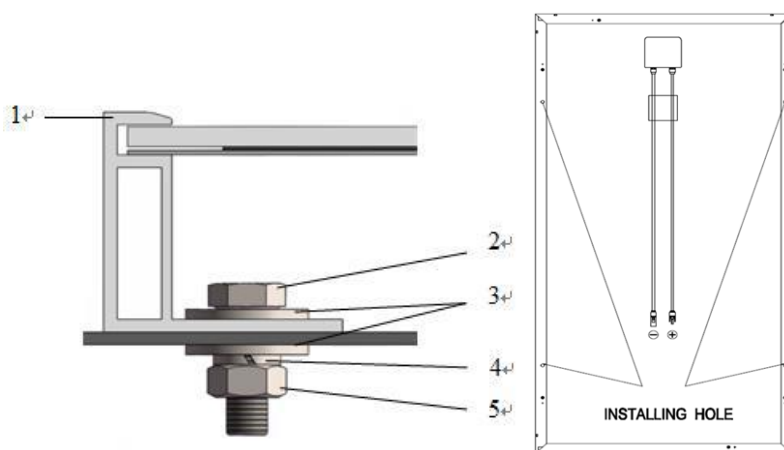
Piezas necesarias para acoplar el módulo a la estructura fija
